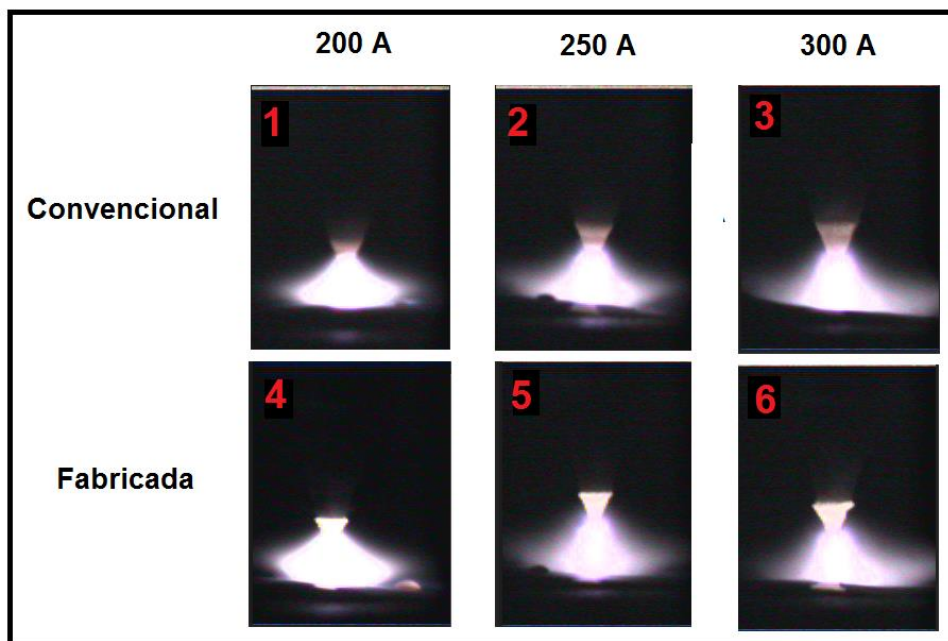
Quadros com imagem do arco de soldagem obtidos a partir da filmagem durante a realização dos testes
